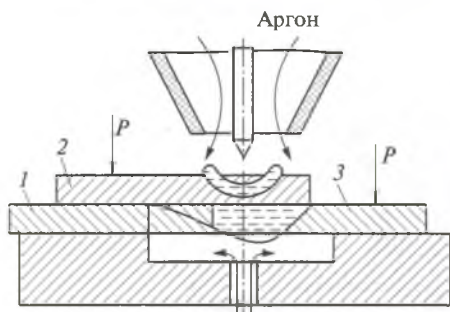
Схема аргонодуговой сварки титана с алюминием с образованием двух отдельных сварочных ванн:
